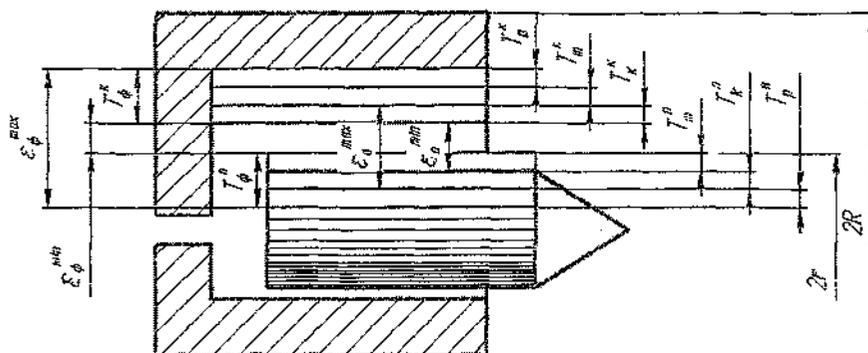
Схема расположения допусков поршневой пары аксиально-поршневой гидромашины
